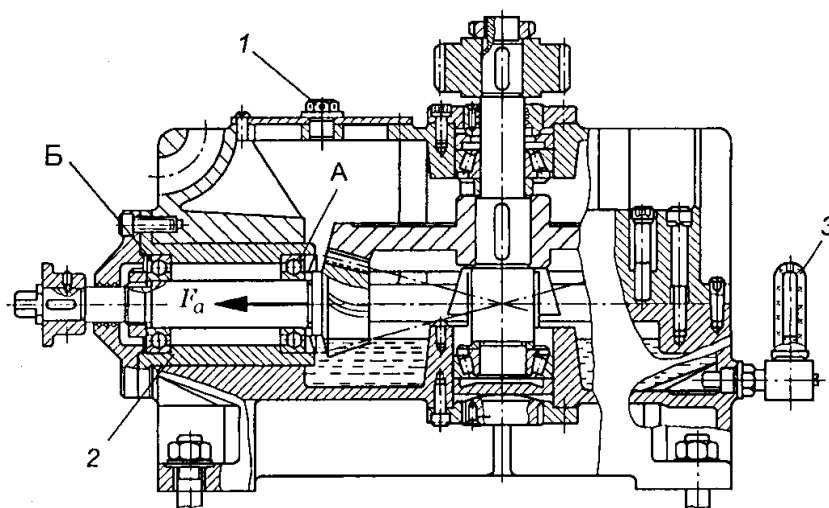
Конический редуктор с вертикальным расположением тихоходного вала:
